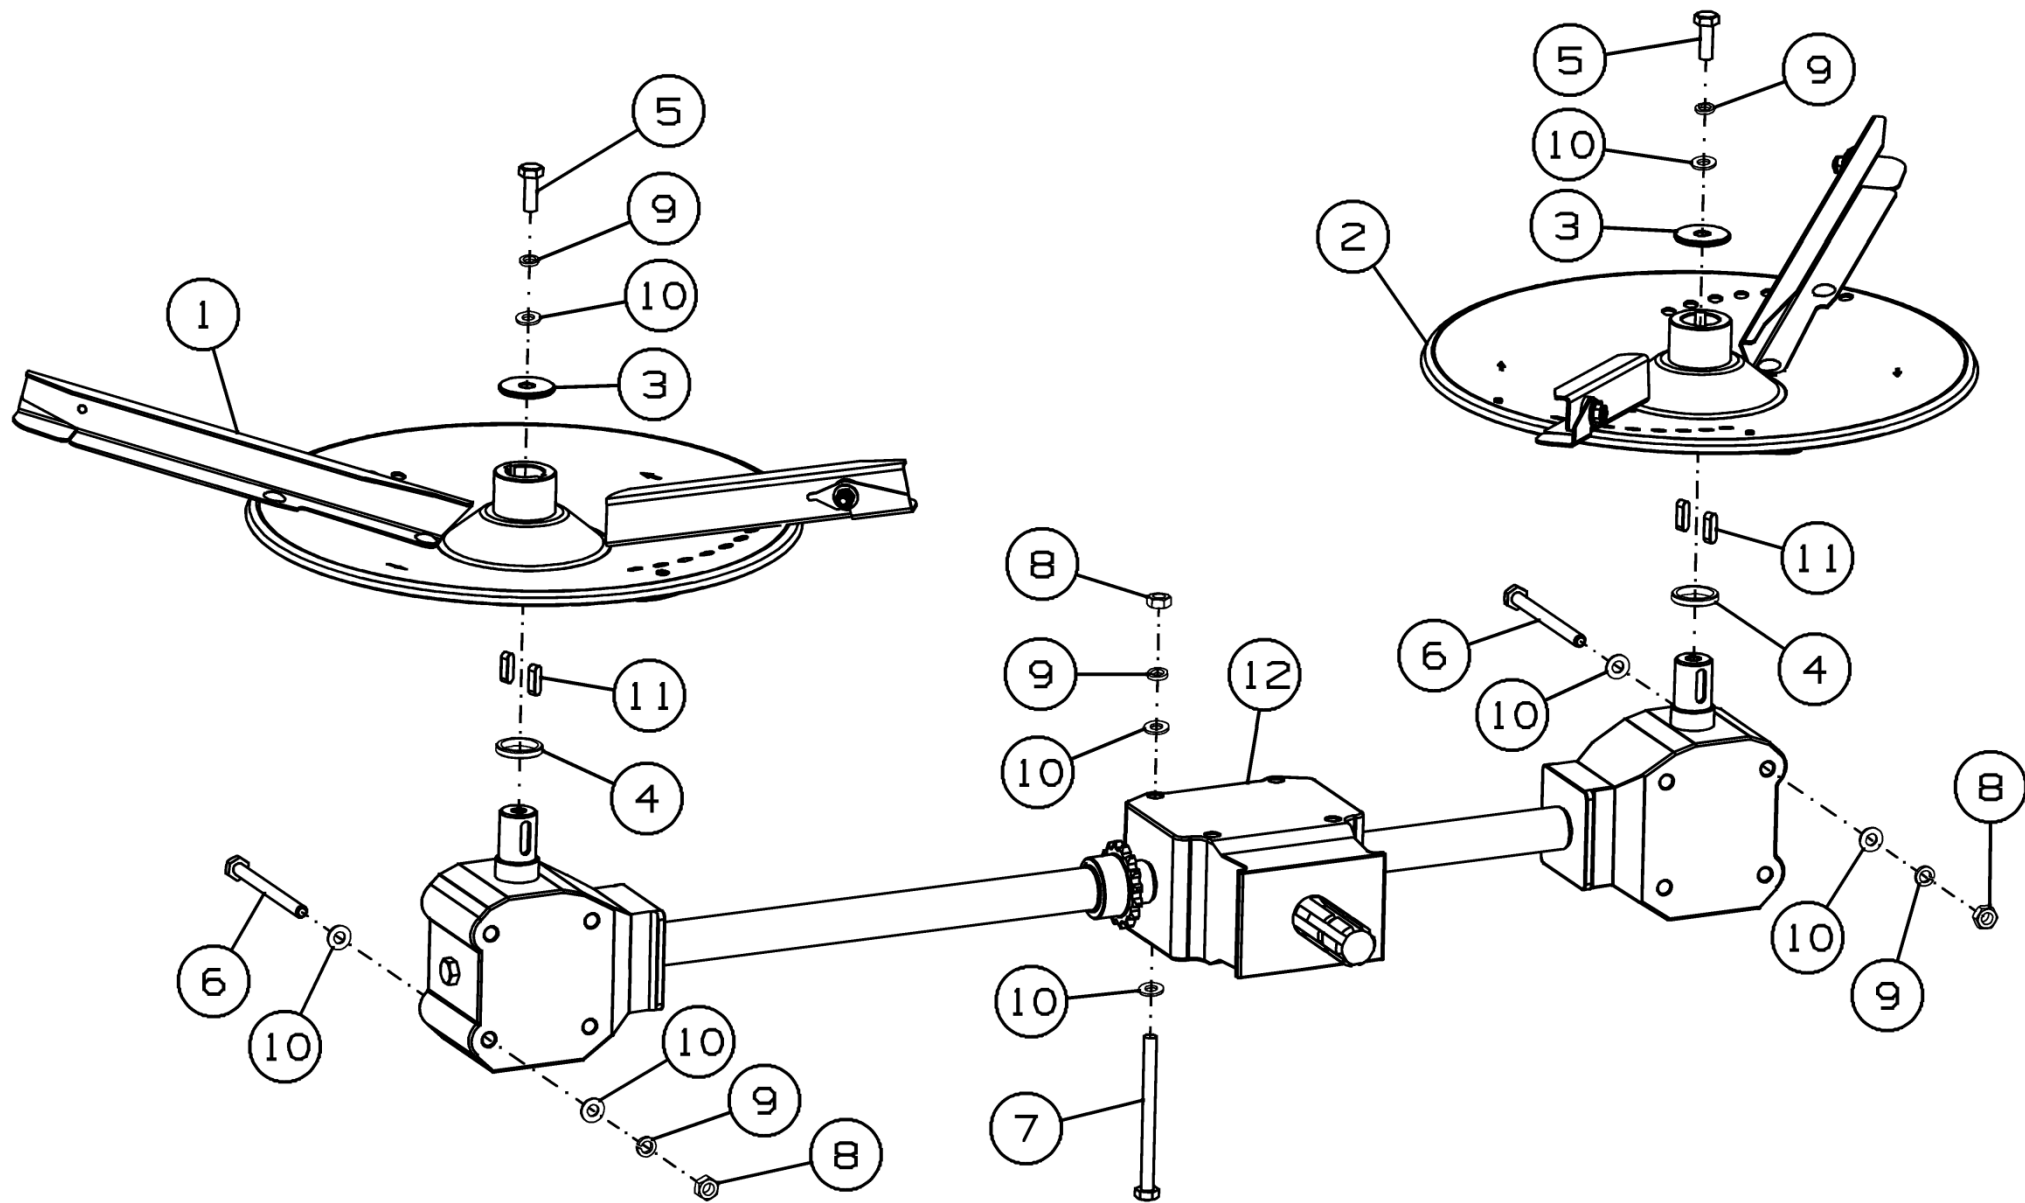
Установка редуктора PA-900.70.00.000Г
